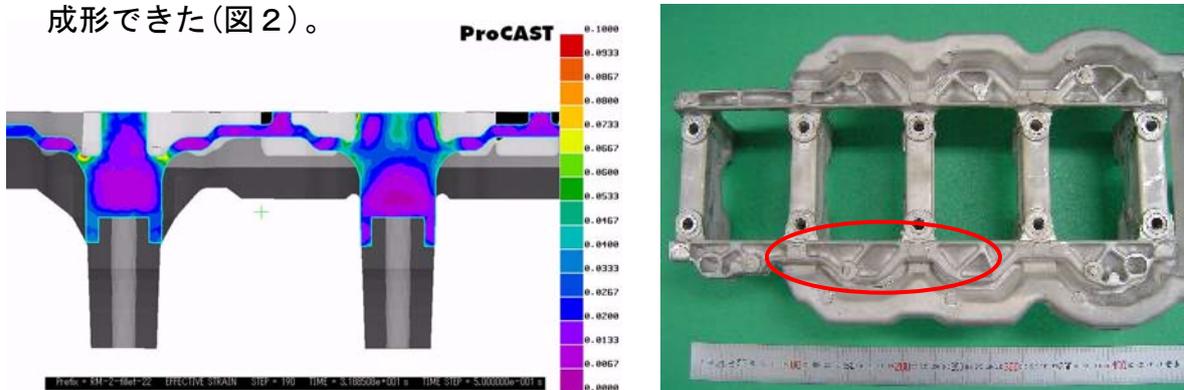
耐熱Mg合金部品「ベアリングビーム」の casting crack 予測と試作結果
